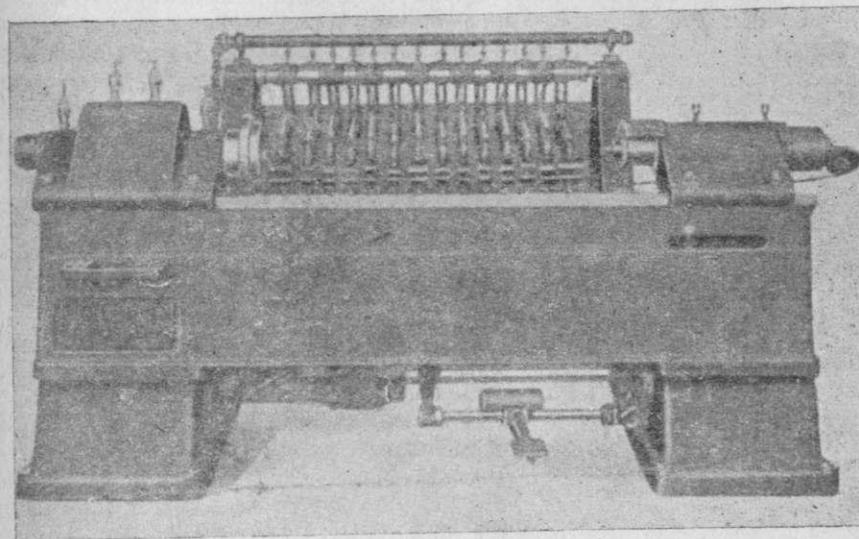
Станок фирмы Нортон для лепинга шеек коленчатого вала.
